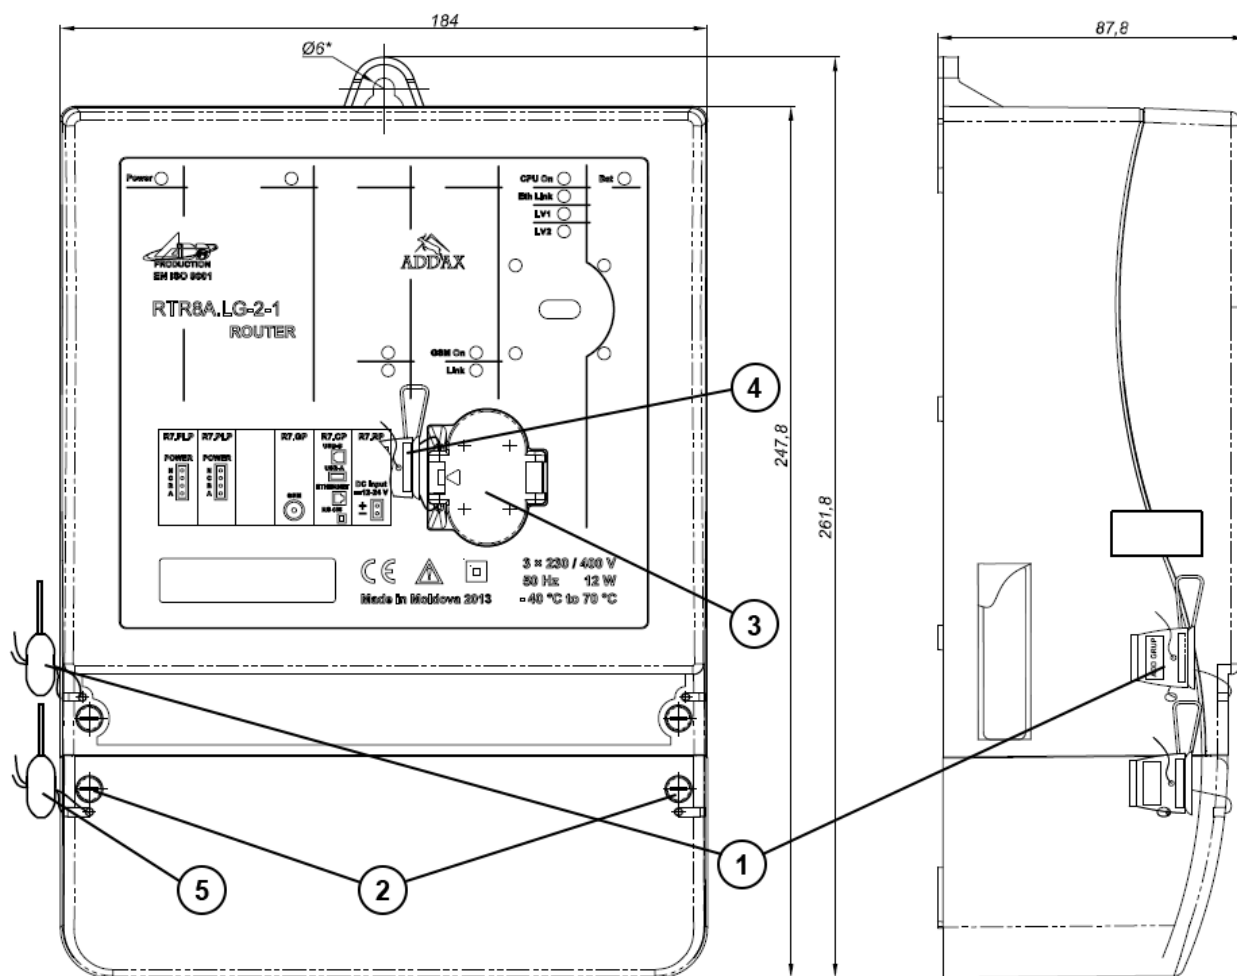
Общий вид и габаритные размеры маршрутизатора (вид спереди - без крышки, вид сбоку - с крышкой клеммника)
